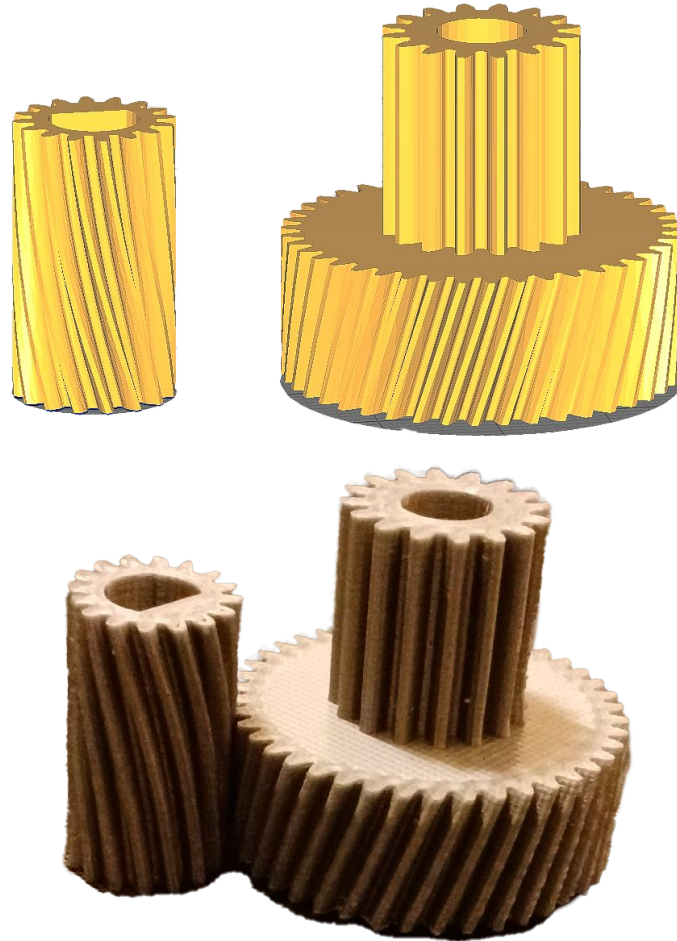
Шестерня валу та ведена нею шестерня редуктора
